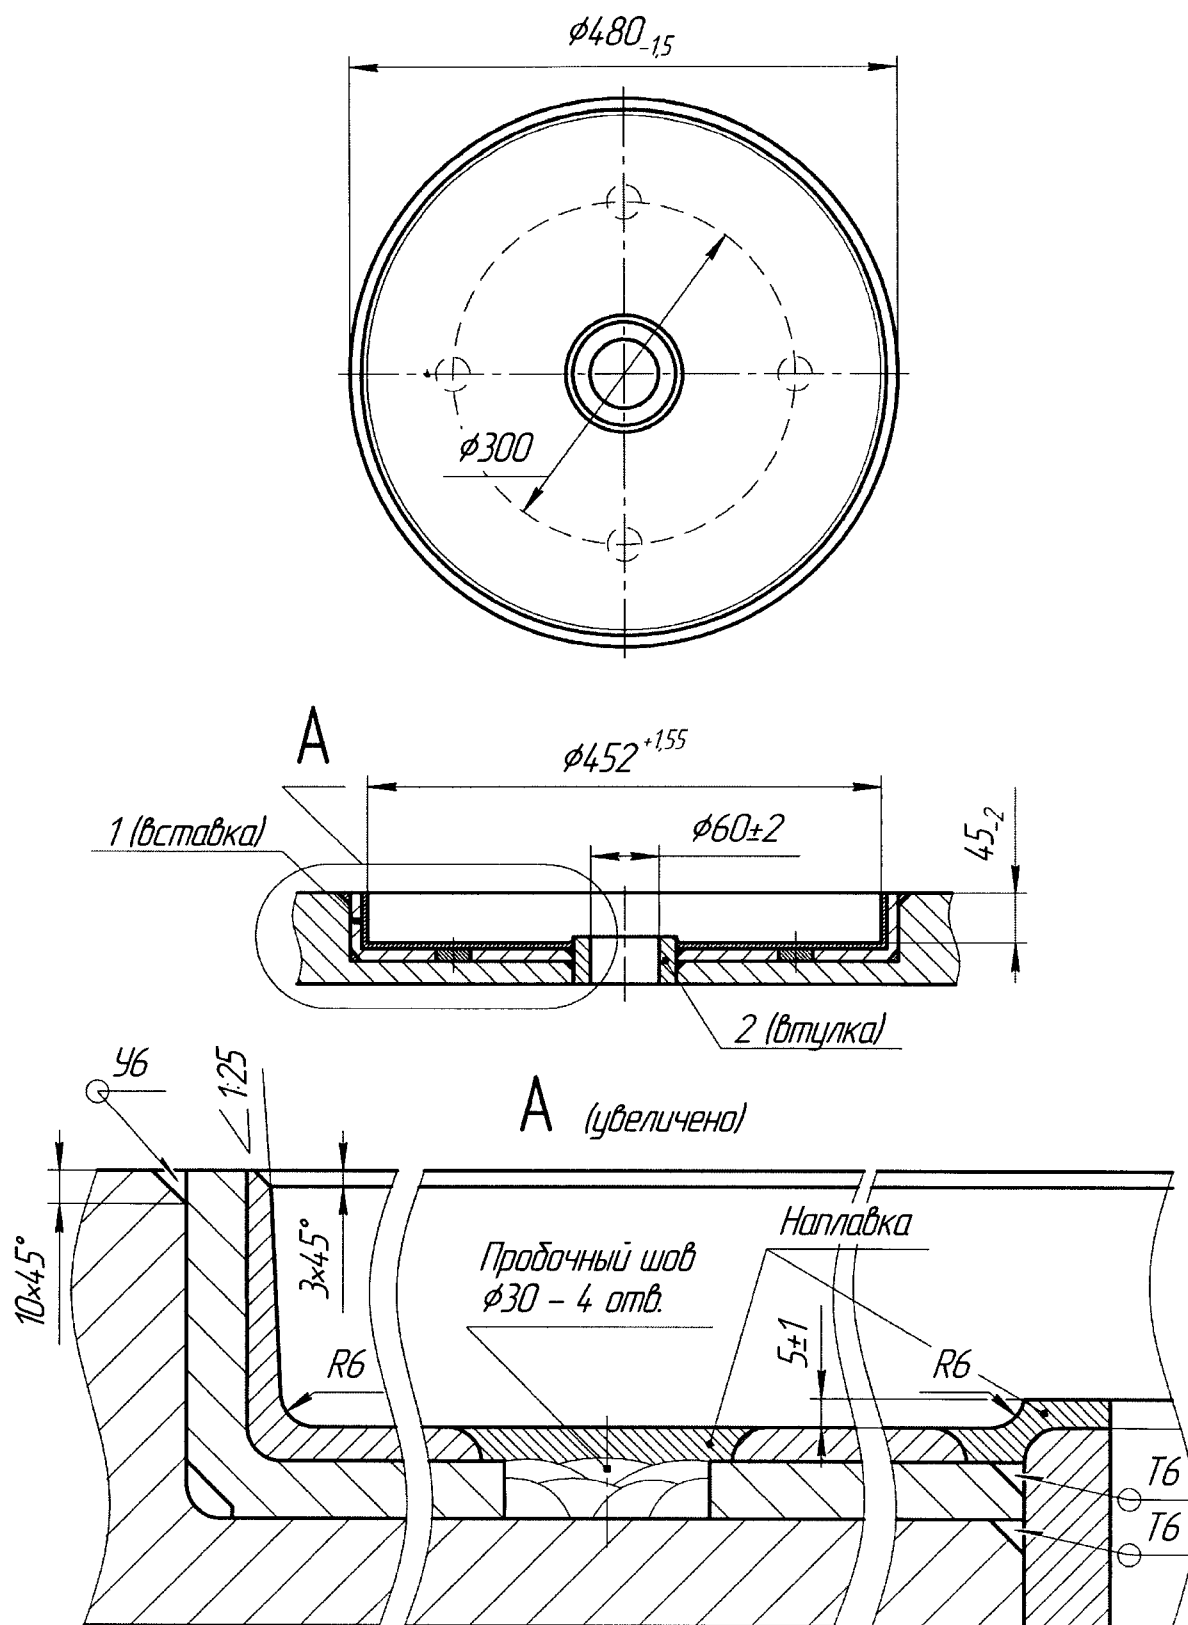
Установка вставки подпятника и втулки с последующей механической обработкой
